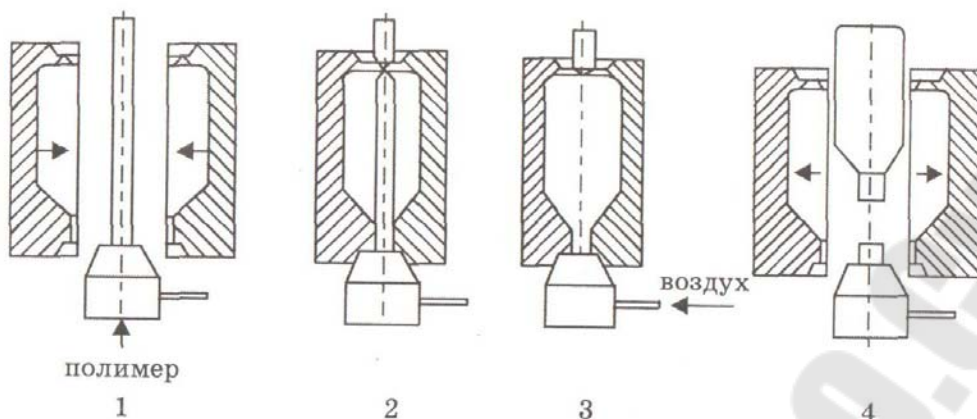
Схема изготовления пластмассовых сосудов методом экструзионного раздува: 1 – экструзия трубчатой заготовки; 2 – сдавливание дна; 3 – раздувание сосуда; 4 – выдувание изделия
